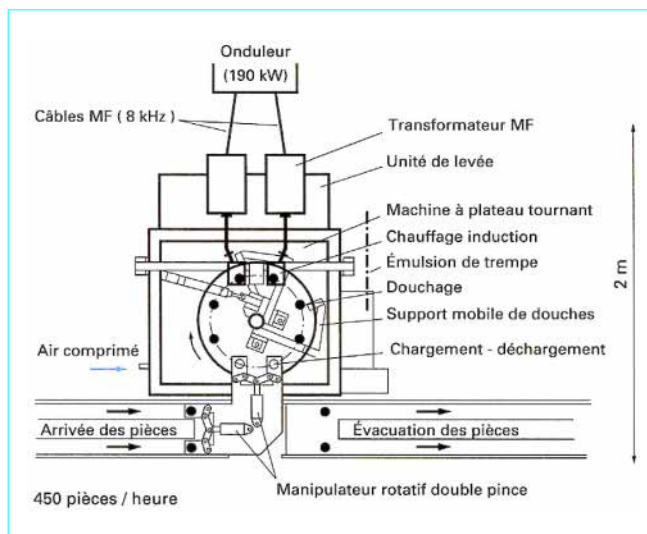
Machine de trempage par induction à plateau tournant pour bols de fusées (vue de dessus)
